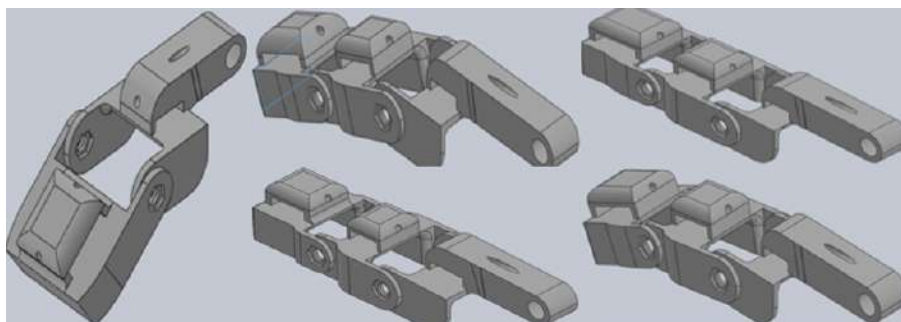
Diseño final del ensamble del dedo índice.
